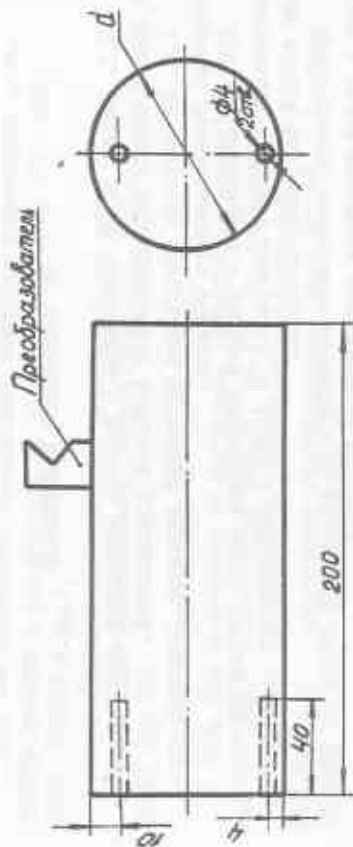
Столбчатый образец для настройки ультразвукового прибора при НК штронах;
